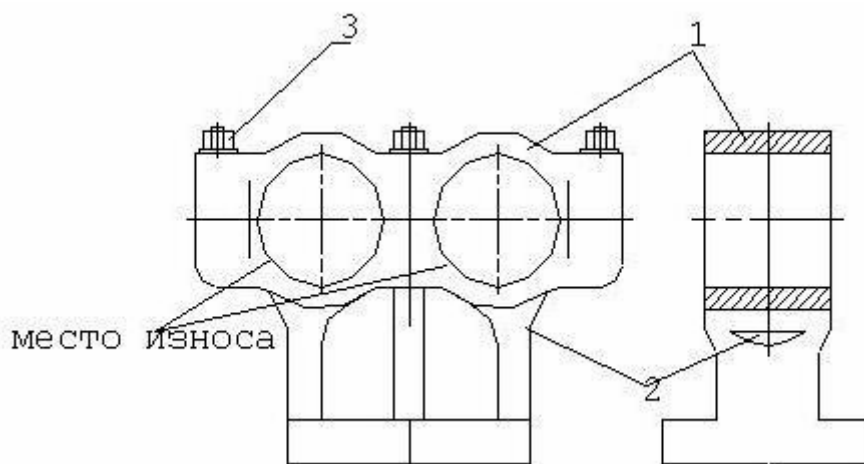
Элементы опорной стойки: 1 – крышка подшипника; 2 – опорная стойка; 3 – гайки крепления
